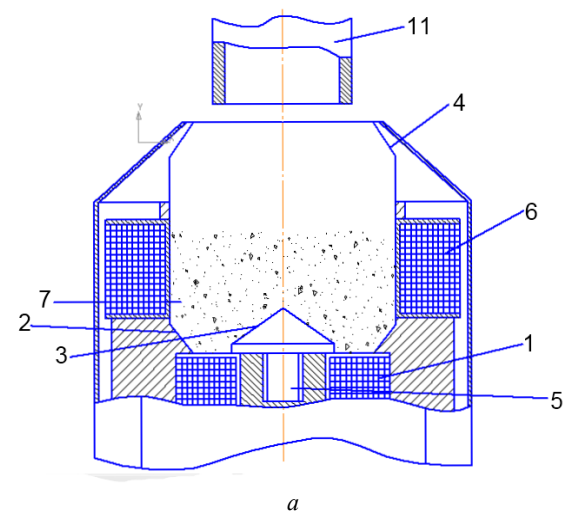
Схема установки для МАО поверхностей деталей машин для обработки червяков
